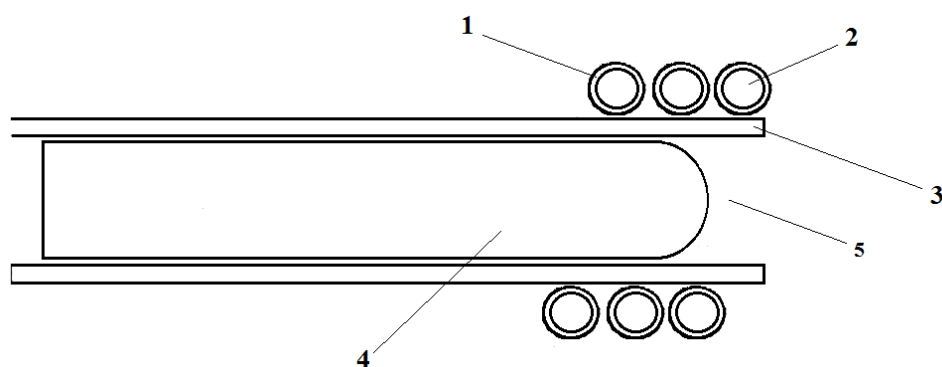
Геометрическая модель камеры для химико-термической обработки, помещенной в индуктор: 1 – индуктор; 2 – вода; 3 – кварцевая трубка; 4 – инструмент из быстрорежущей стали; 5 – азотосодержащая среда
